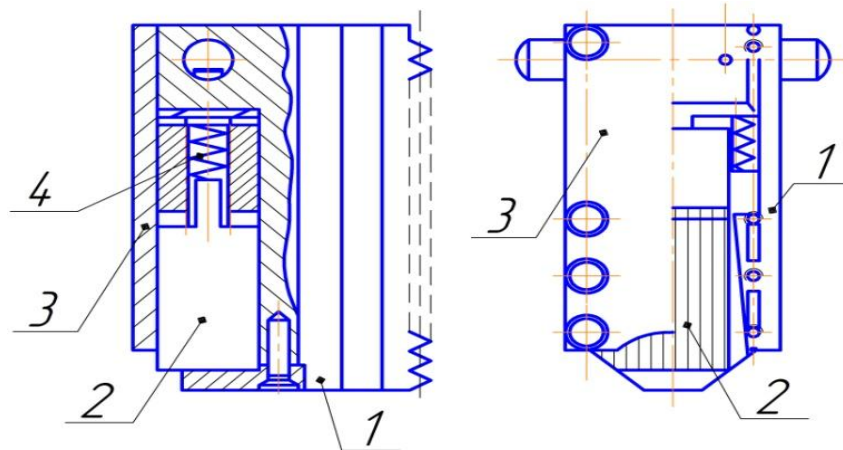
Адаптивний затискний кулачок із зоною адаптації у вигляді підпружинених пластин: 1 - корпус кулачка; 2 - набір пластин; 3 - кришка; 4 – пружина
